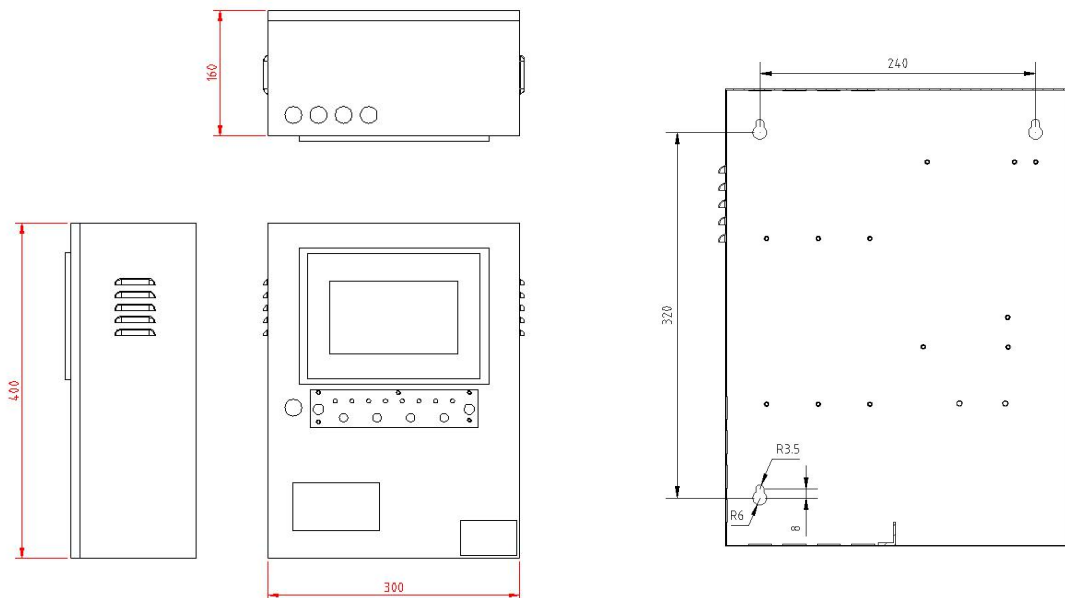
AFRD100/B3 型防火门监控器外形尺寸和安装尺寸图
